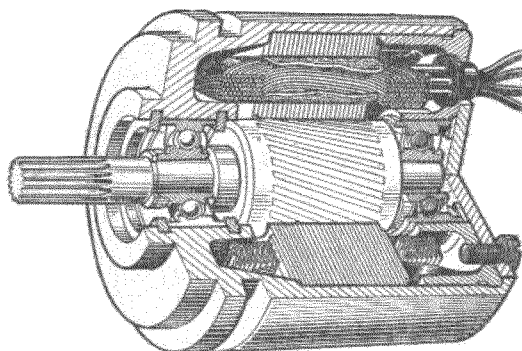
Асинхронный исполнительный двигатель сквозной конструкции
